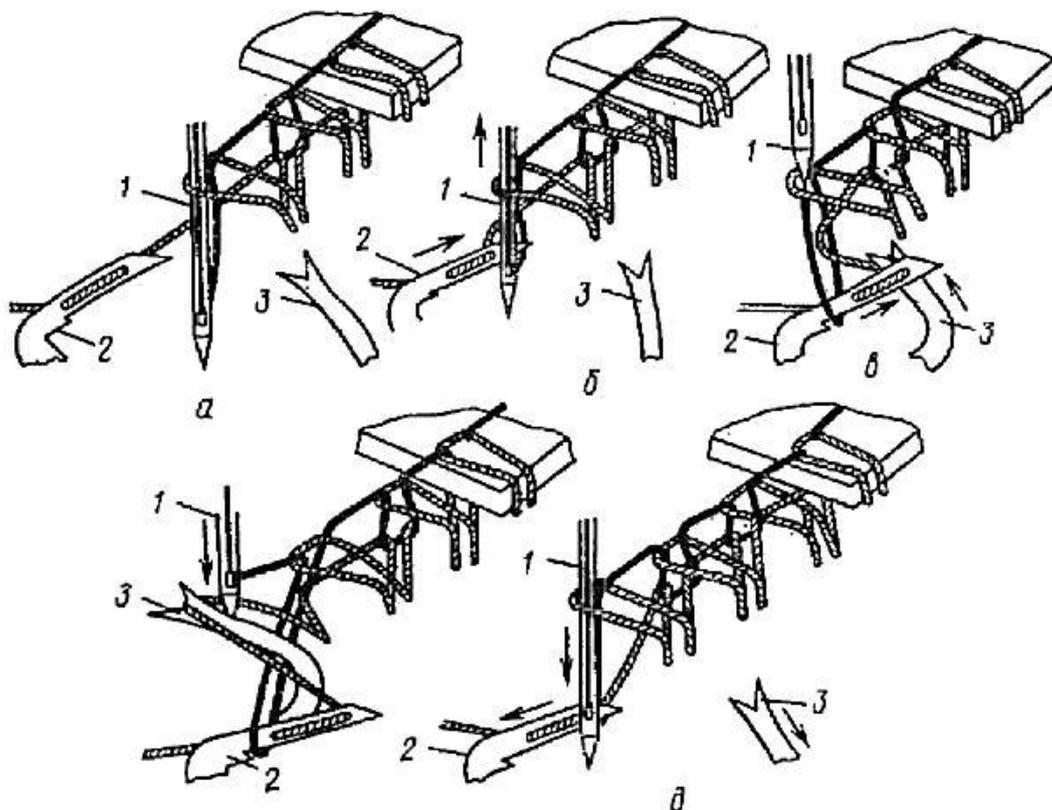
Принцип образования двухниточного цепного обметочного переплетения
